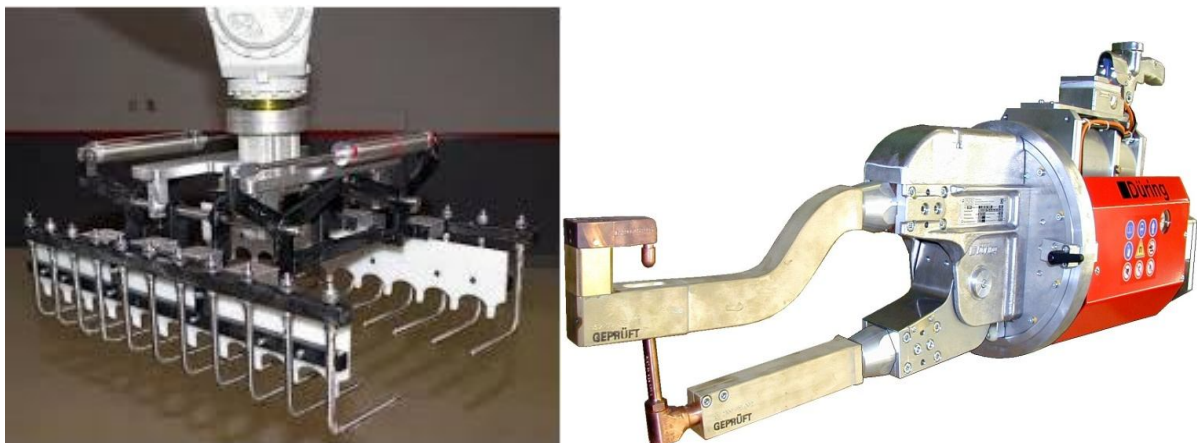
Приклади робочих органів: захватні пристрої, зварювальні кліщі [1]
